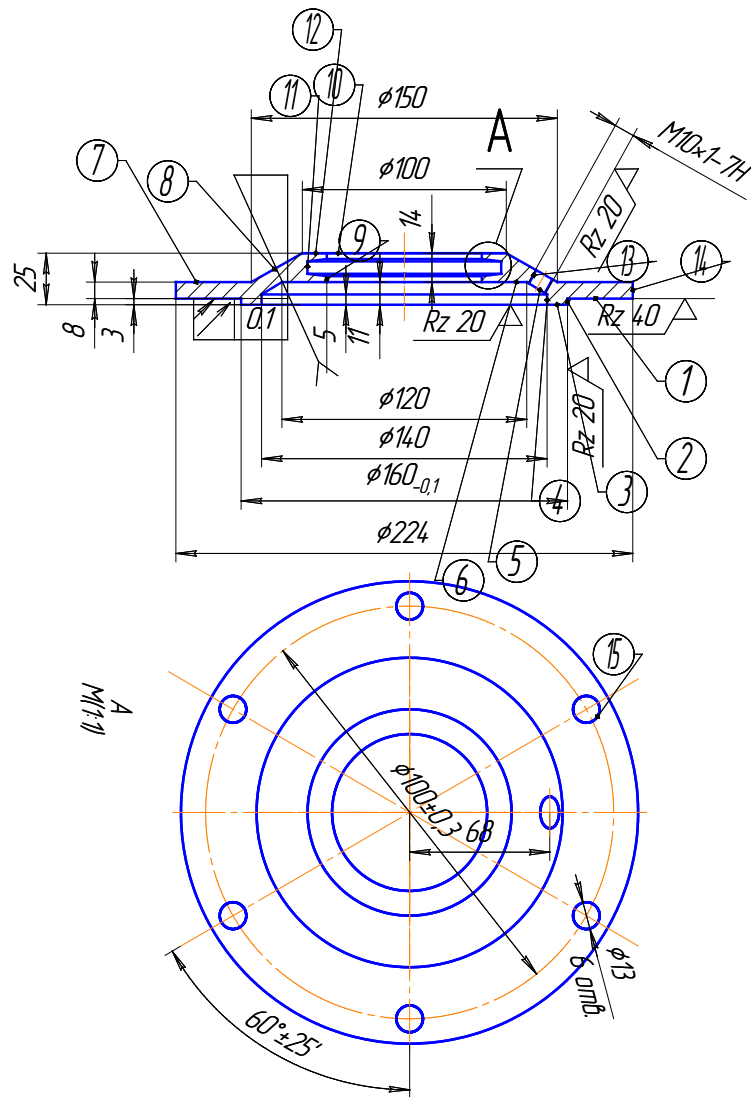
Нумерація оброблених поверхонь деталі кришка
